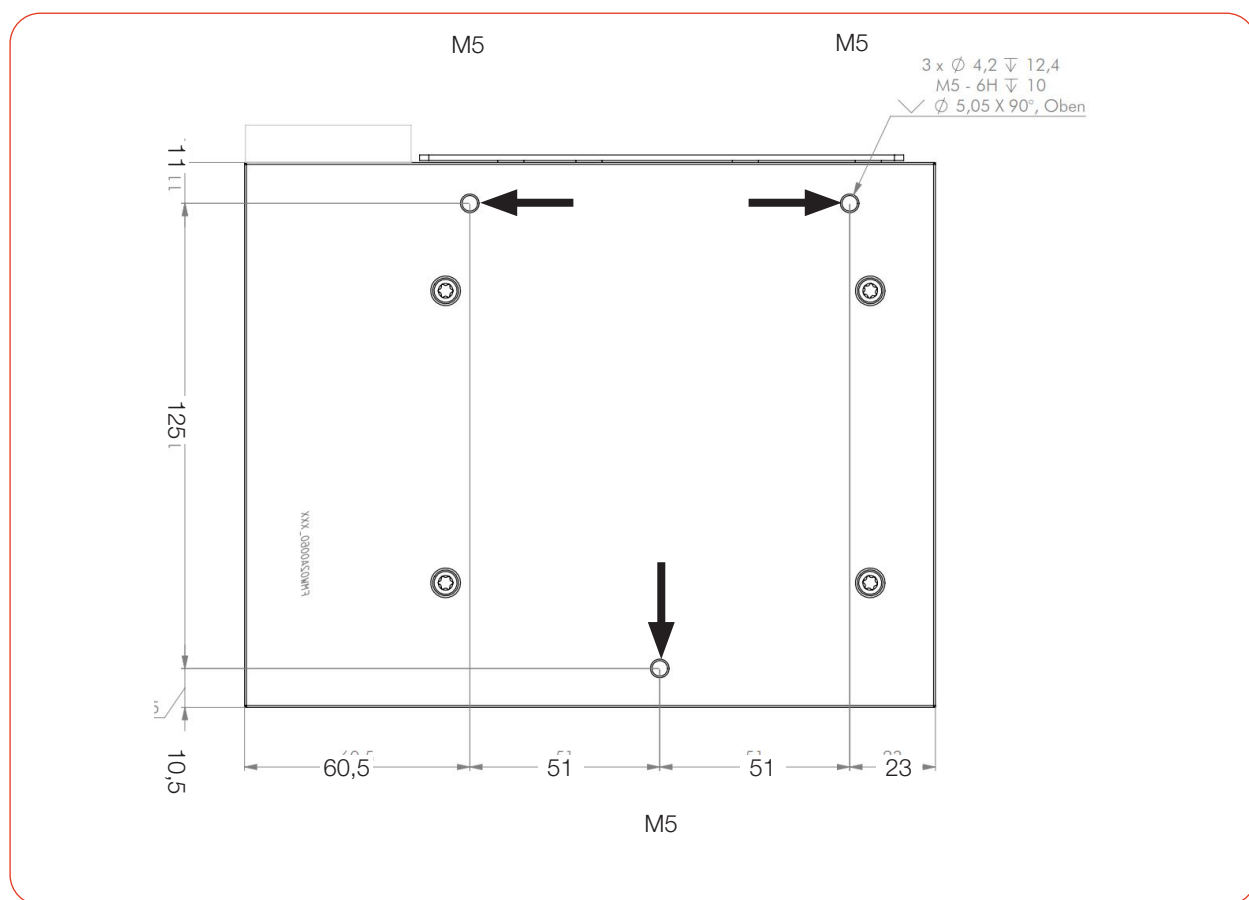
Befestigungsgewinde an der Unterseite des FMW+ R2
